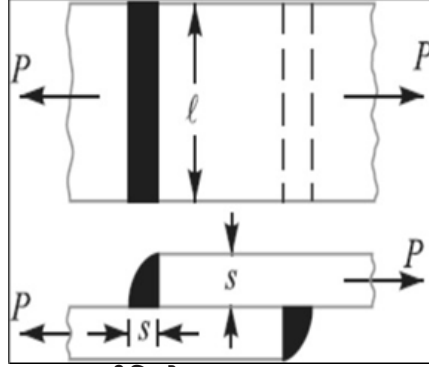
डबल ट्रान्सव्हर्स फिलेट (Double Transverse Fillet Weld)
